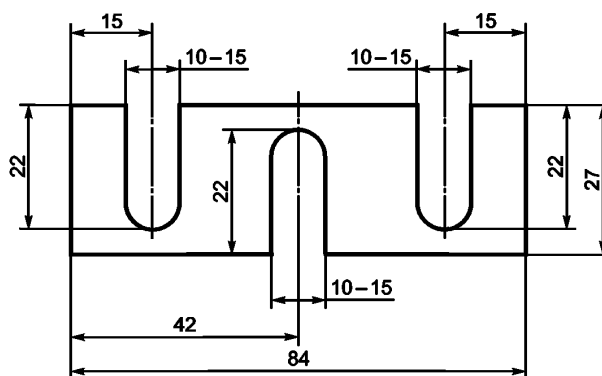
Пластина — держатель карты (контактная поверхность)
